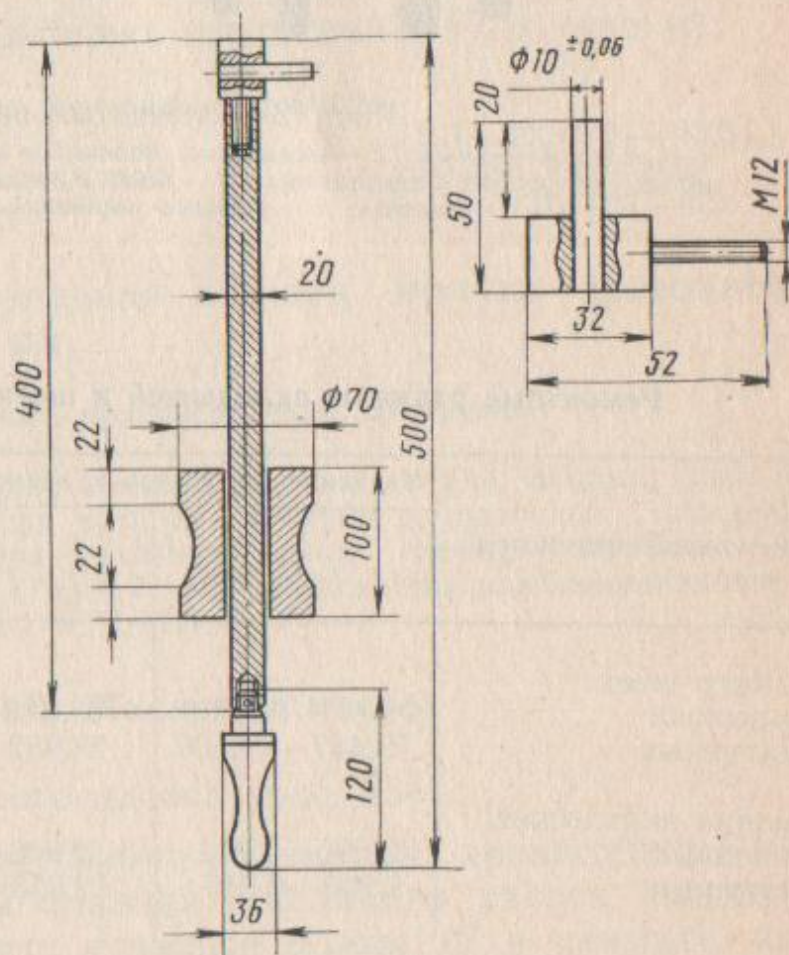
Приспособление для выпрессовки крышек коренных опор коленчатого вала
